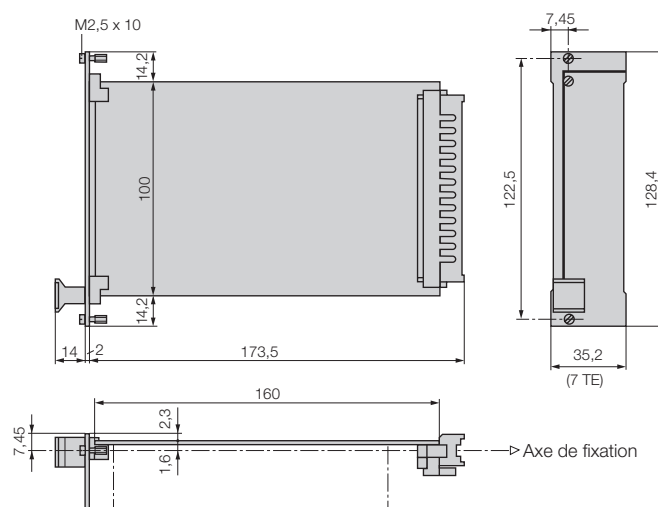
EURAX F 534, largeur de la plaque frontale 7 TE.
